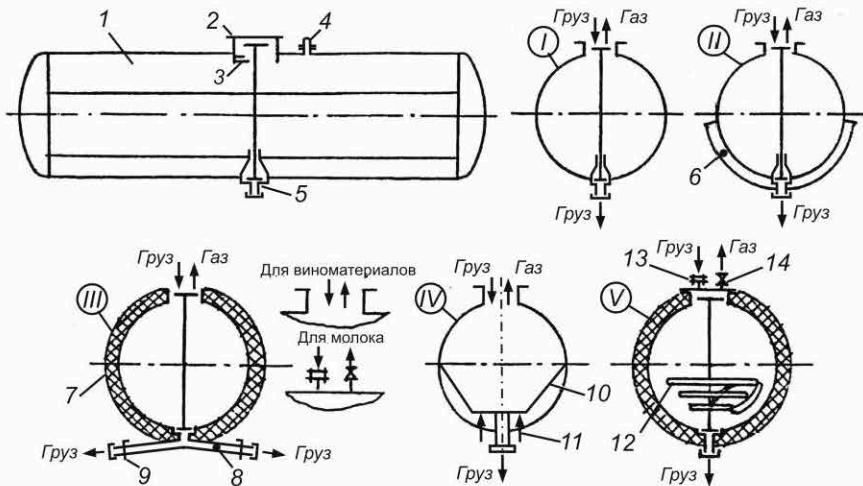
Схемы котлов с верхним открытым способом загрузки и нижним выгрузки:
